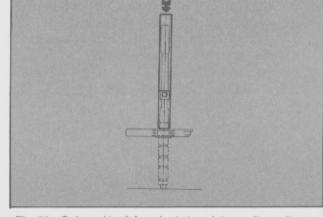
Colocación del conjunto tapa intermedia - cojinete.
